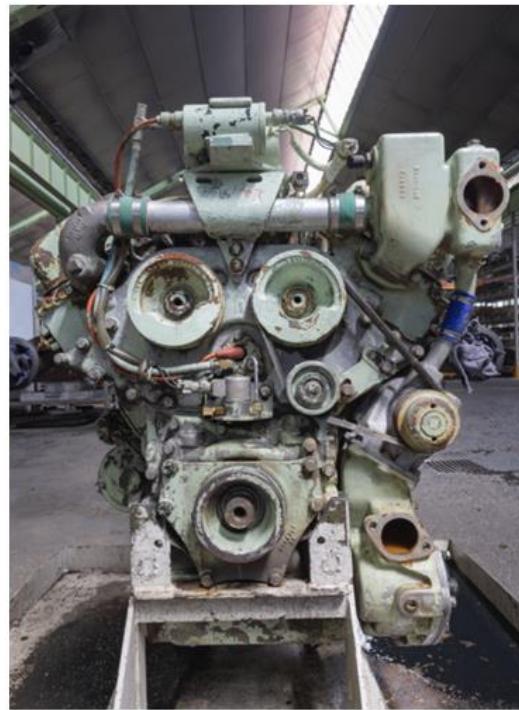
Motor del TOA. Fuente: PCMASA 2.
